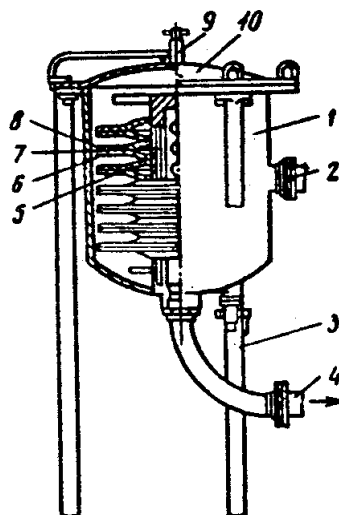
Дисківий фільтр: 1 – корпус; 2 – патрубок для входу молока; 3 – стійки; 4 – патрубок для виходу молока; 5 – циліндрична склянка; 6 – фільтруючий елемент; 7 – отвір; 8 – диск; 9 – клапан для випуску повітря; 10 – кришка.
